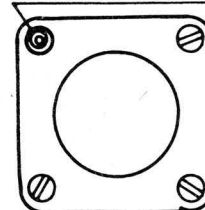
Der angeschlossene Drucktank, zumeist mit rundem oder viereckigem Querschnitt. Das Anschlußrohr für die Druckleitung im Tank darf nur gerade hineinreichen, damit durch die Druckleitung kein Kraftstoff angesaugt wird
